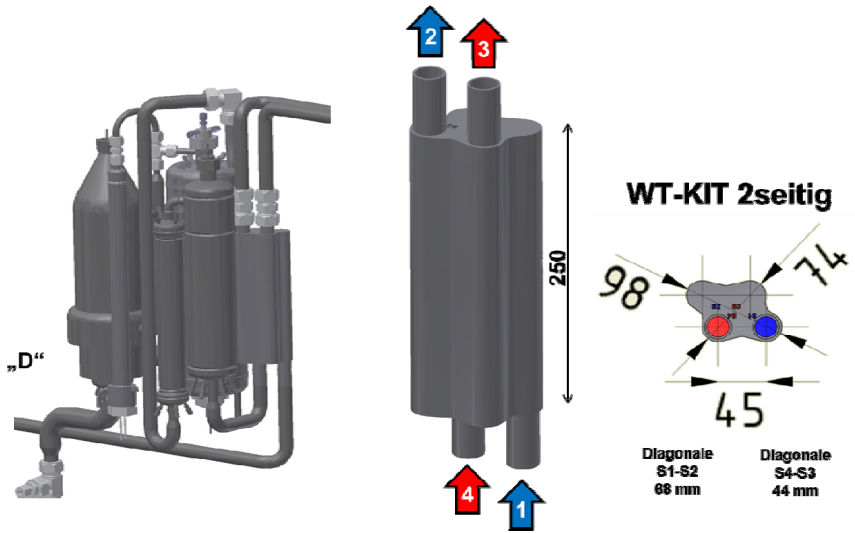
Modulversion „D“ mit technischen Details zum Wärmeaustauscher des KIT (zweiseitige Anschlüsse).
